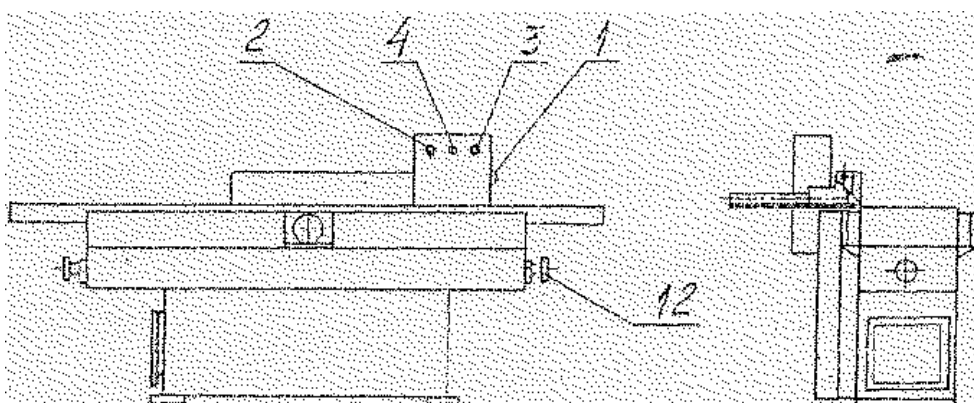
Общий вид станка СФ4(К) с обозначением органов управления
